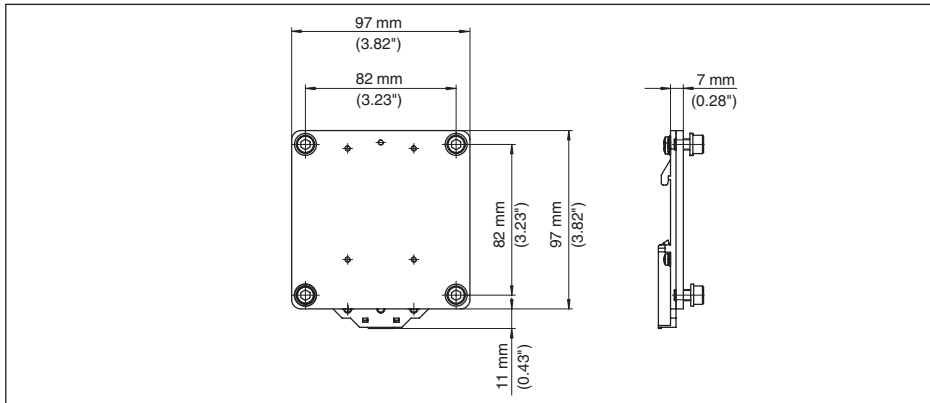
Placa adaptadora para montaje en regletas de montaje del VEGADIS 82
